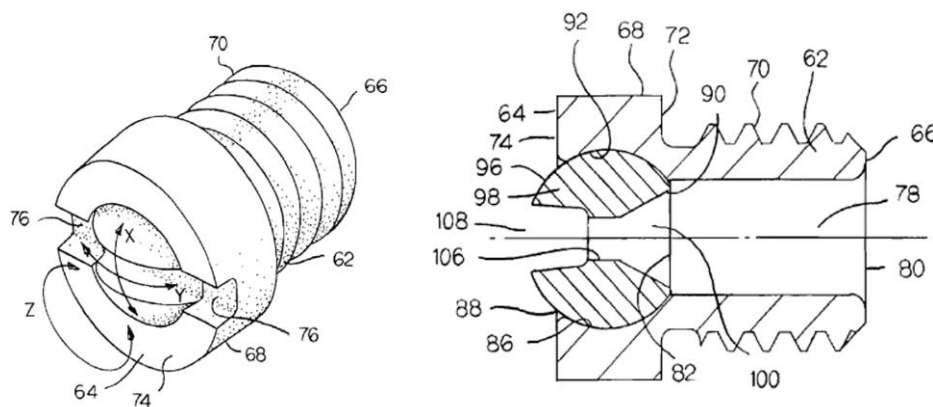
Patent nástroje s regulovatelným chlazením [53]
